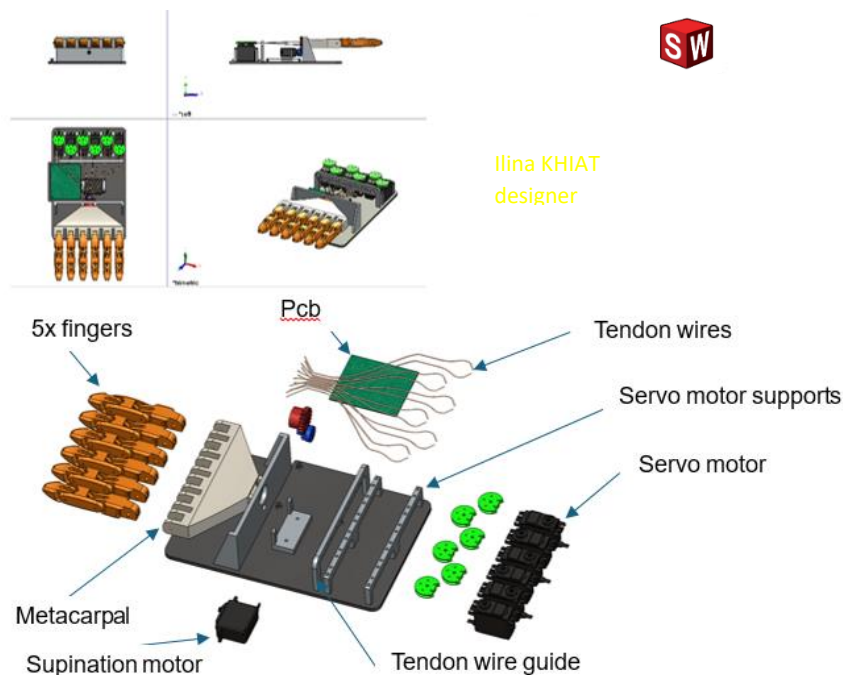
Images montrant la "forme de main robotique" assemblée en première projection angulaire, en vue 3D isométrique et en vue éclatée (design doigt 2).
